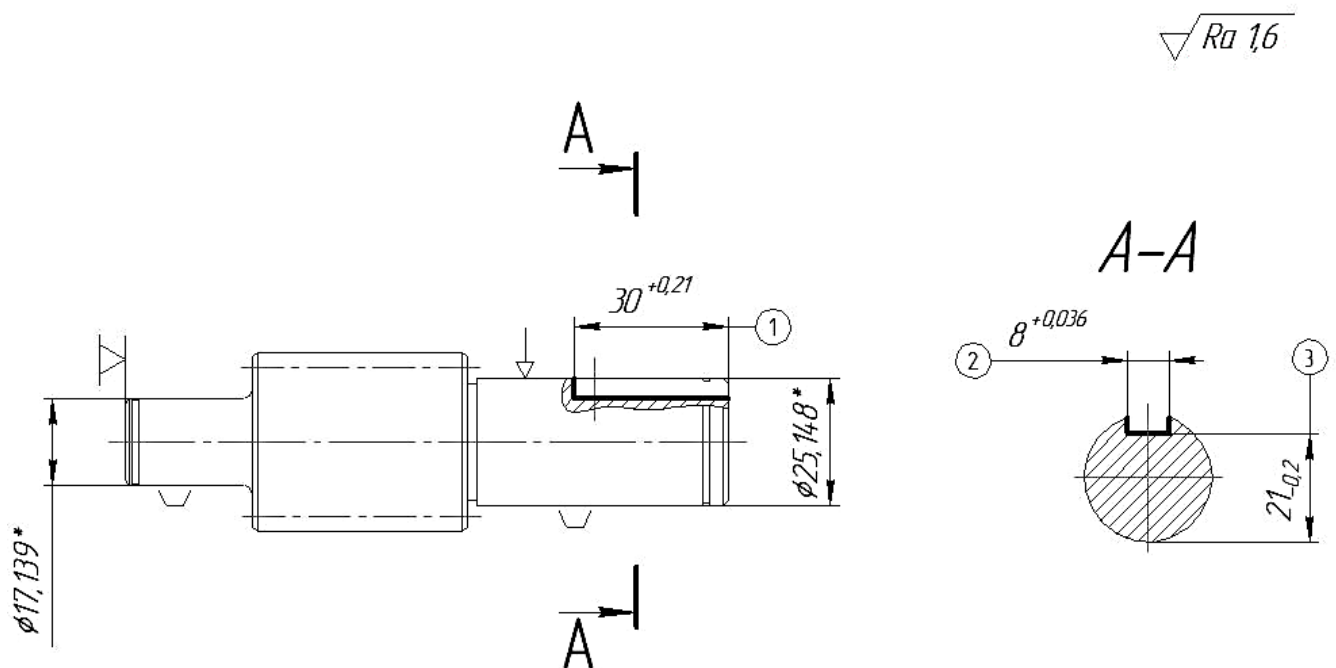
Ескіз до обробки на операції 065 – фрезерна з ЧПК
